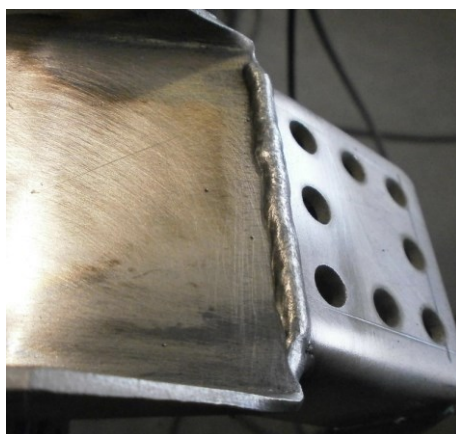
Sestehovaný díl připravený ke svařování [22]
